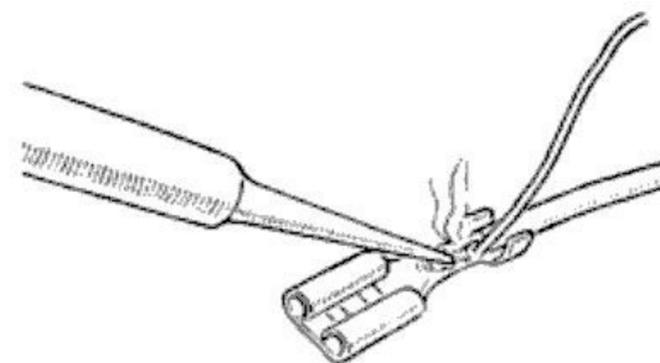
Modo de proceder a la soldadura de un terminal de tipo Faston.
